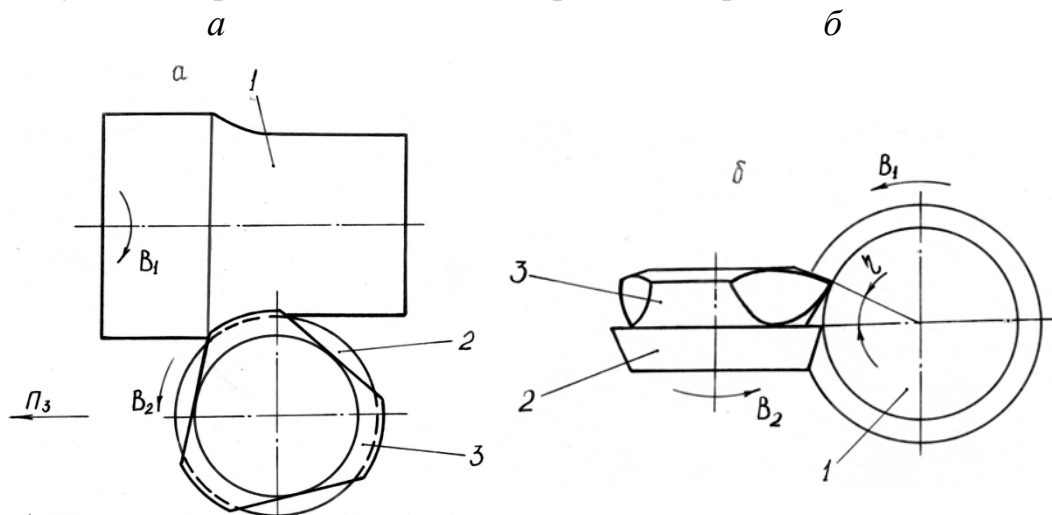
Кинематическая схема обработки (а) и схема установки комбинированного инструмента (б) при совмещении процессов частичного и полного формообразования цилиндрической поверхности
